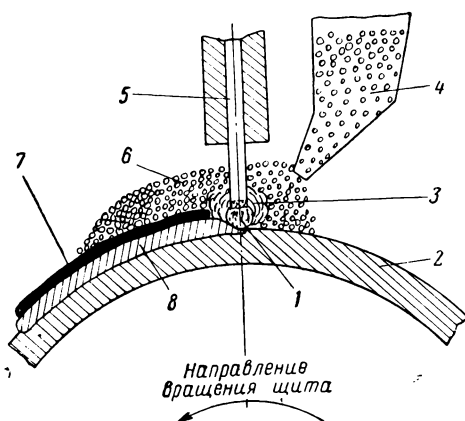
Наплавка подшипникового щита под слоем флюса:
